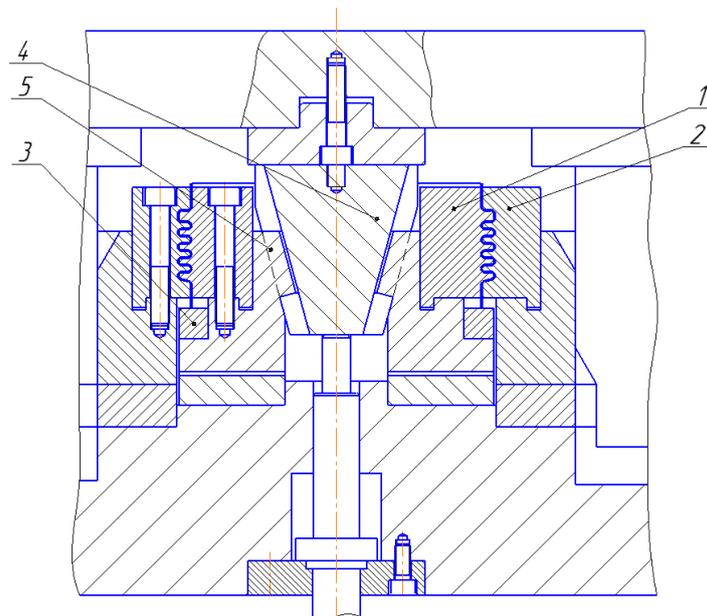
Чертеж инструментального штампа: 1 – Сектор внутренний; 2 – Сектор наружный; 3 – Фиксатор; 4 – Пуансон; 5 – Матрица; Плита верхняя – 6; Плита нижняя – 7; Втулки – 8; Колонки – 9.
